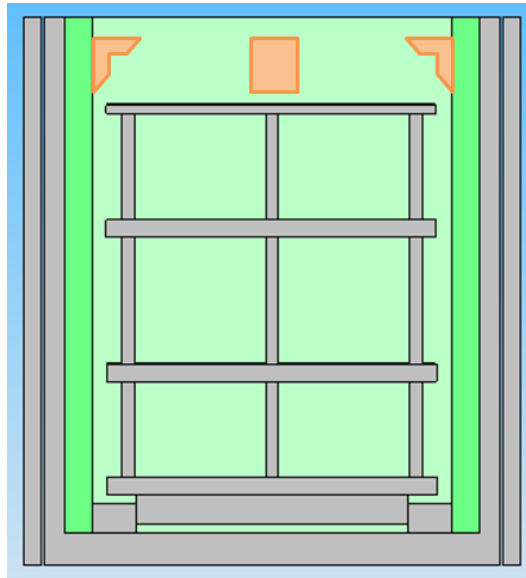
24: Detalle de la colocación de las escuadras en el interior de la estructura móvil
